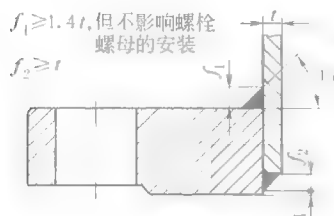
板式平焊法兰和平焊环板式松套法兰与钢管的焊接连接
